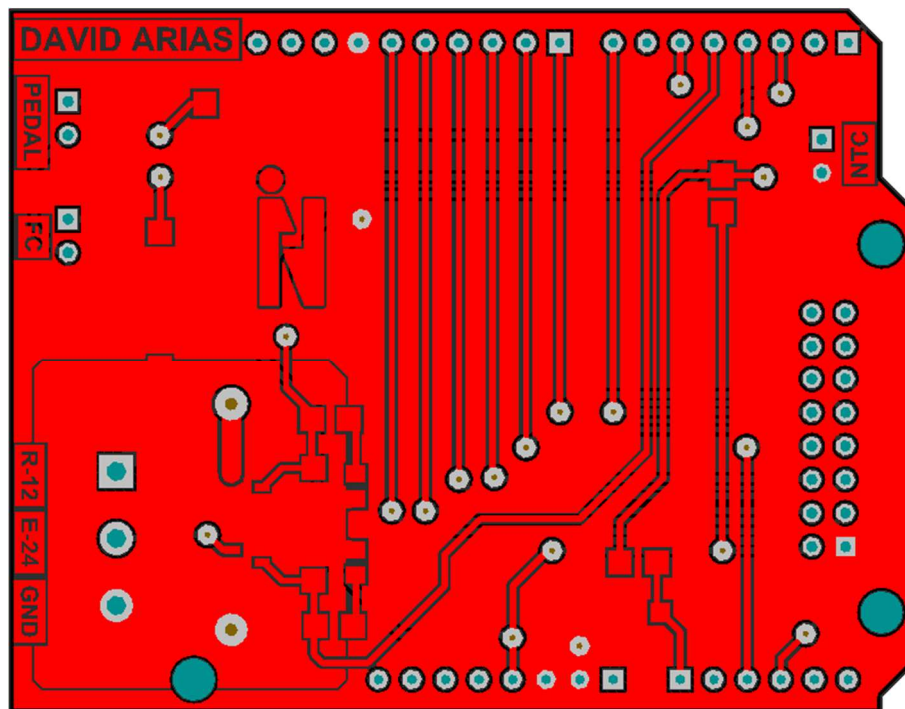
Diseño de la cara superior (*TopLayer*) de la PCB de control
